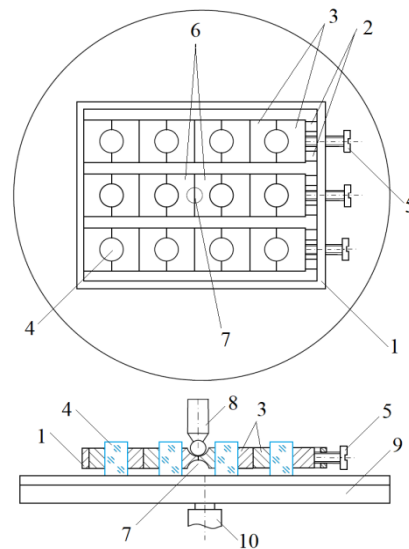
Устройство для шлифования и полирования оснований заготовок цилиндрической формы
